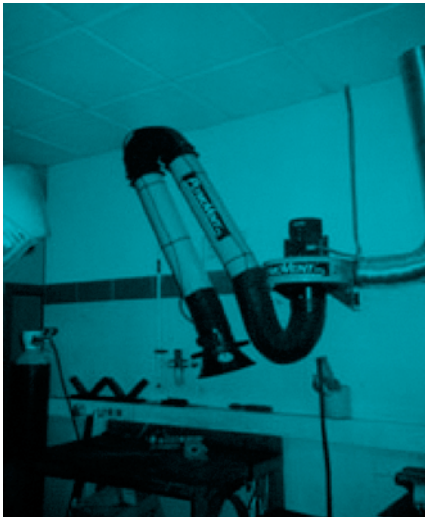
Sistema de extracción localizada para soldadura.
